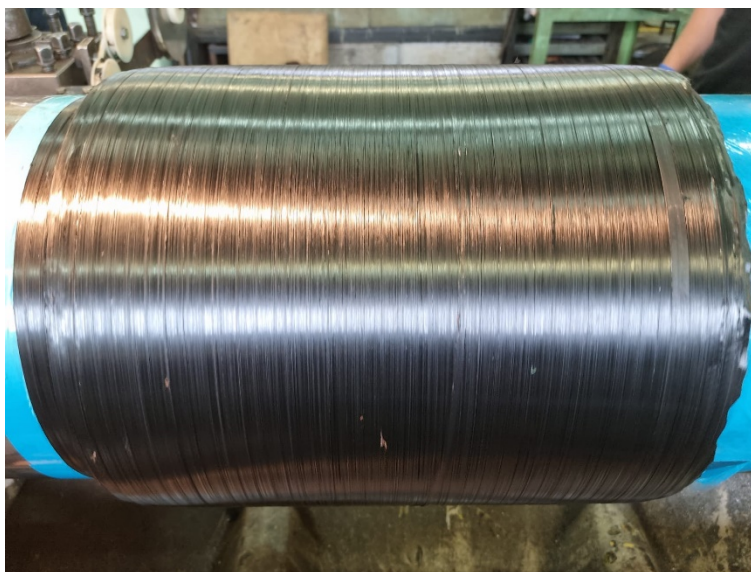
Фотография намотанной заготовки для изготовления макета корпуса
